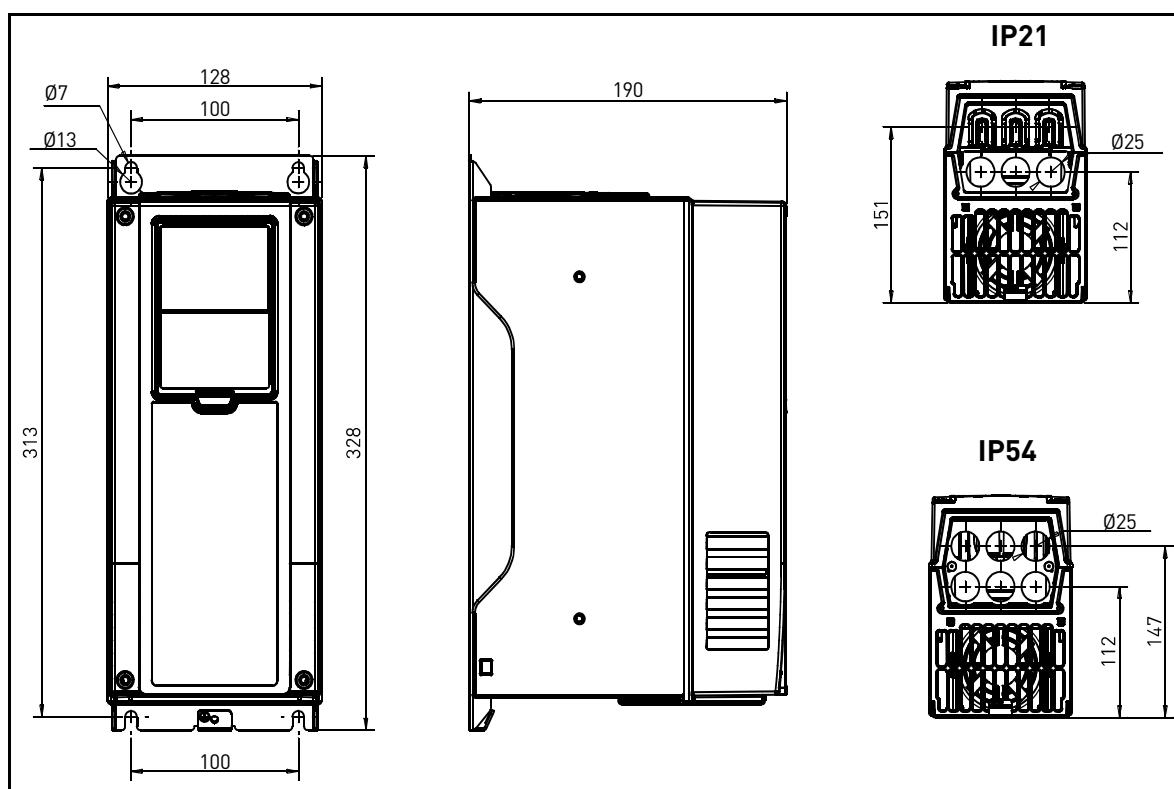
Dimensões do inversor de CA Vacon, MR4, montagem na parede
